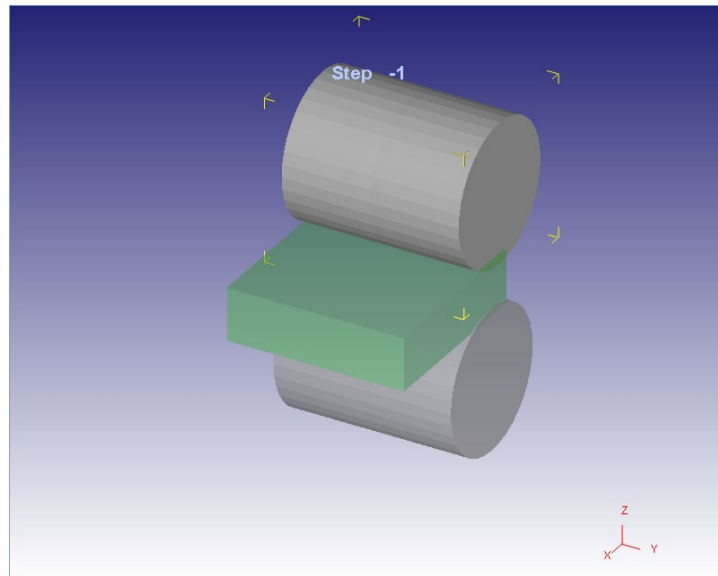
Схема розташування прокатних валків та оброблюваного матеріалу
